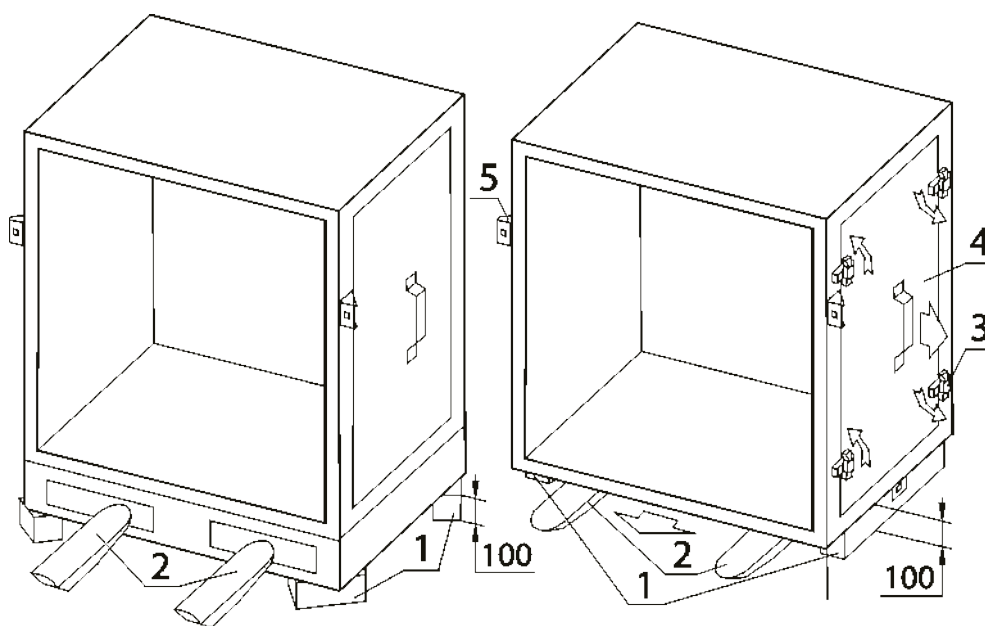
Расположение секции на вилах погрузочного приспособления:
